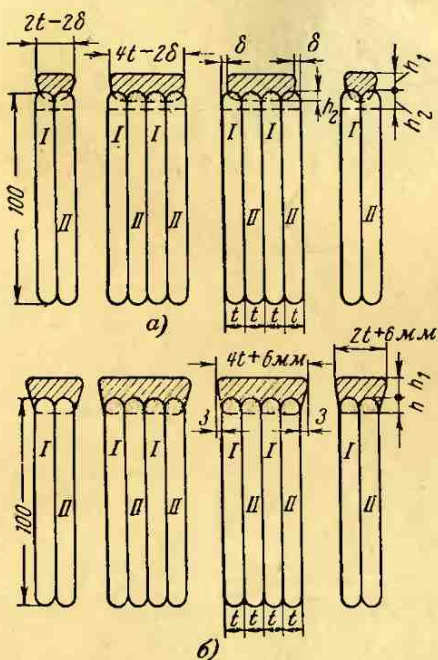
Сварные швы соединения шин магистральных шинопроводов.
